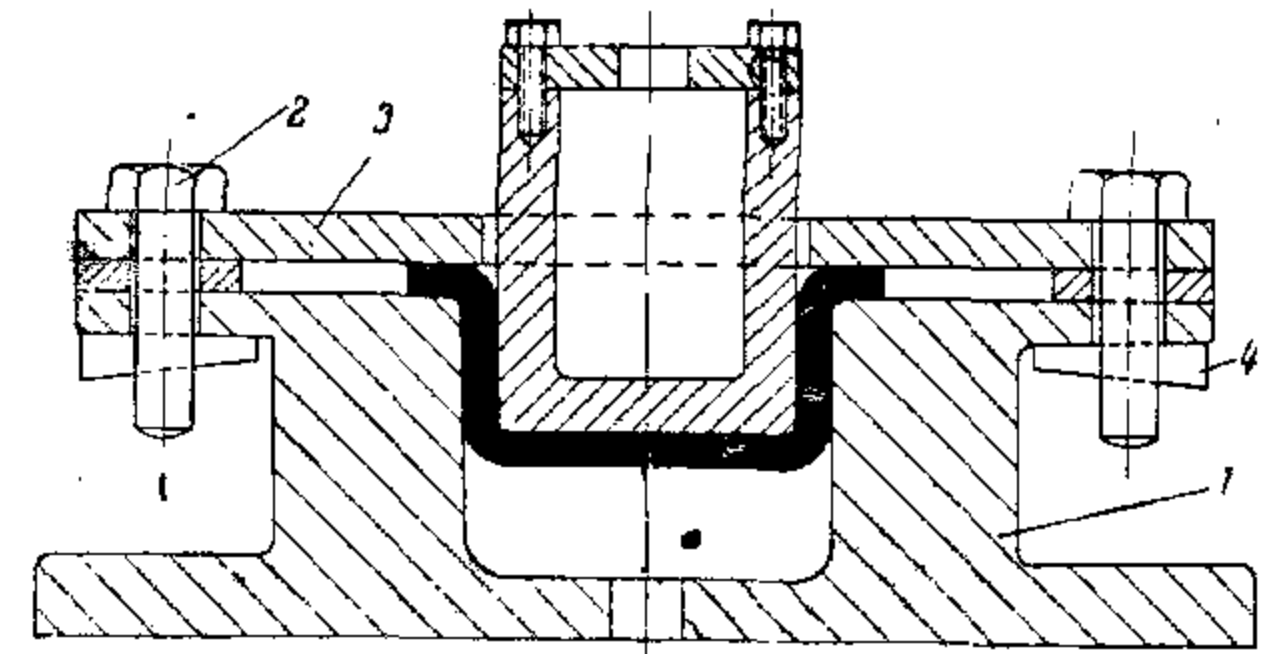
Штамп с клиновым креплением прижима для глубокой вытяжки на одноходовом прессе
